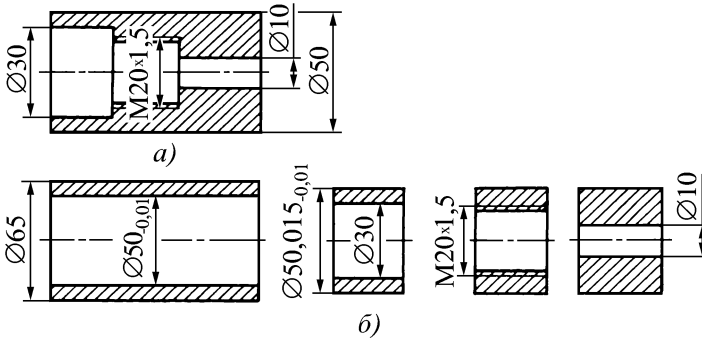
Внутренний цельный (а) и сборный (б) калибры соосности
